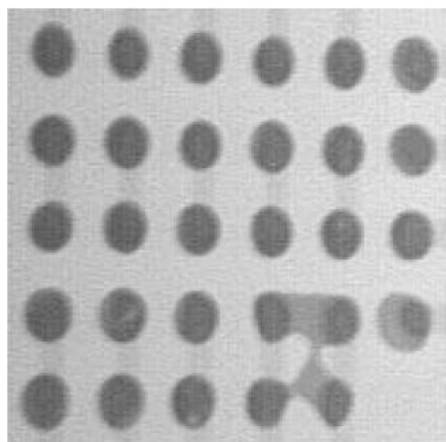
Fotografía de rayos X de uniones de soldadura 63Sn/37Pb mostrando puentes temporales [2].
